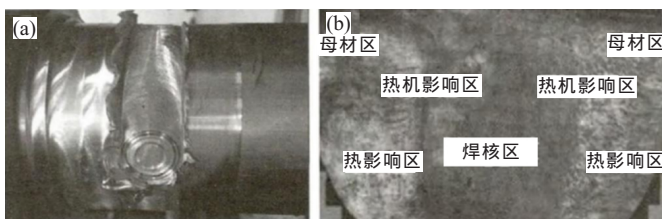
液压油缸的FSW焊缝表面及焊接接头横截面的宏观形貌^[40]
